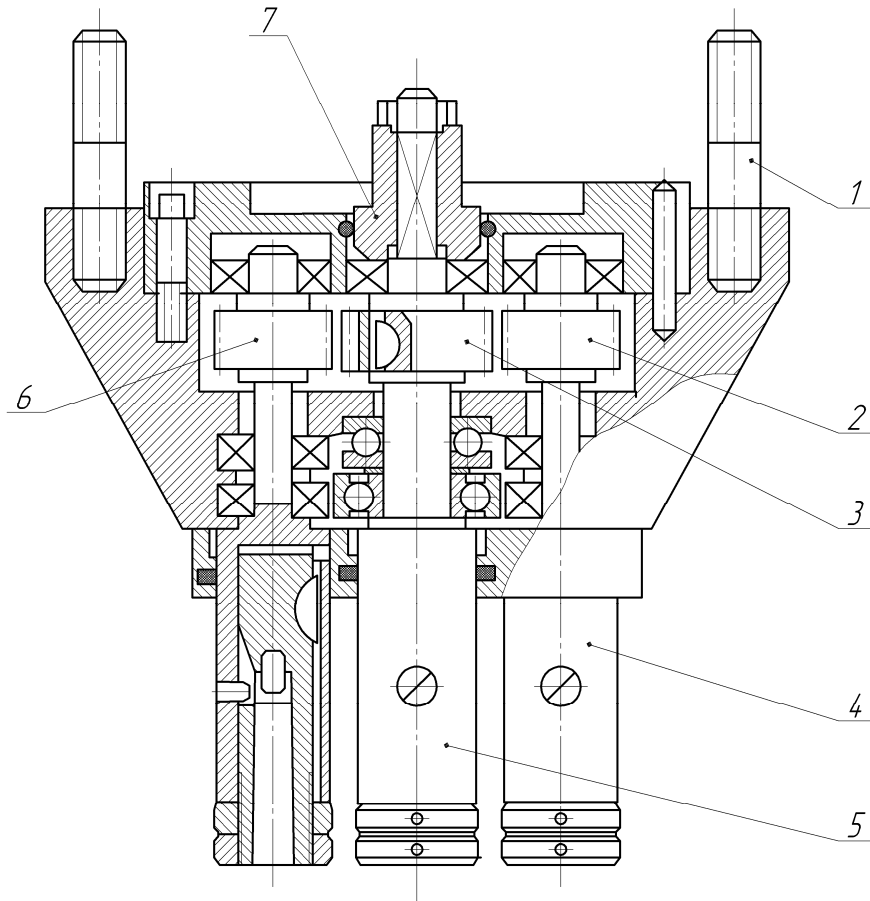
Будова тришпindelної свердлильної головки з одноярусним розташуванням зубчастих коліс: 1 – шпилька; 2, 3, 6 – зубчасті колеса; 4, 5 – шпинделі; 7 – втулка
